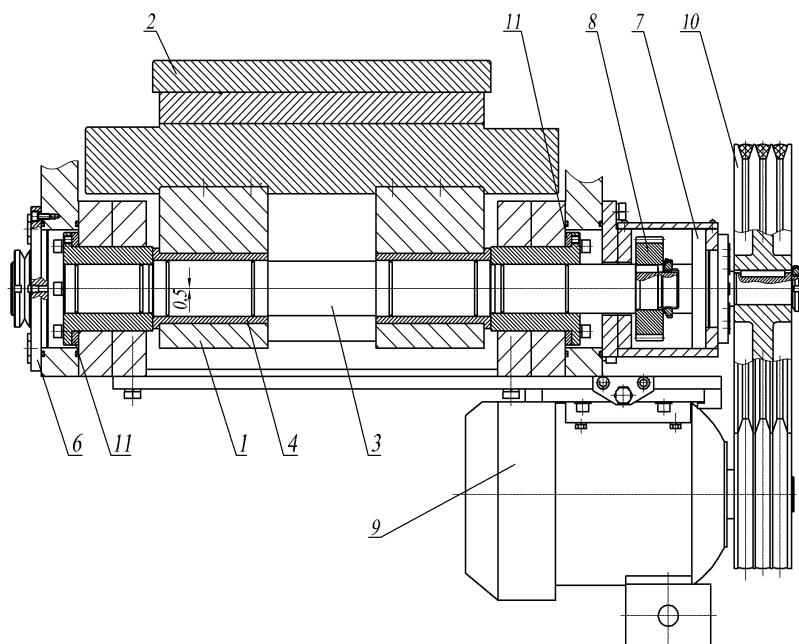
Дополнительный привод стана реверсивной поперечной прокатки
